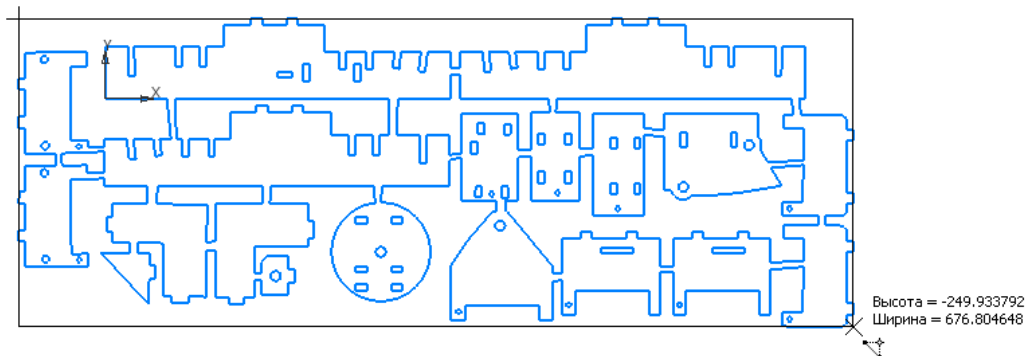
Эскиз деталей для изготовления стапеля для стального сварного кулака
